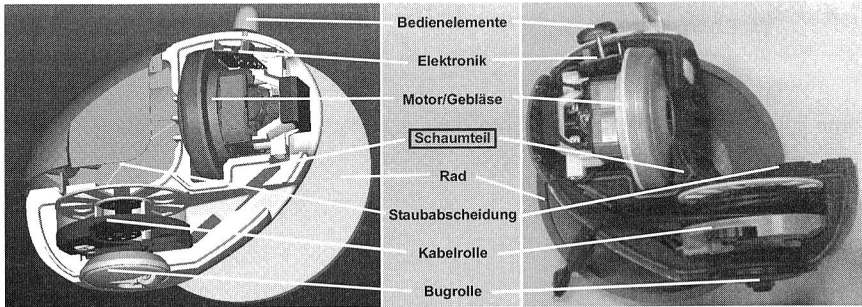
Detailansicht einer Gehäusehälfte mit aufzunehmenden Komponenten
